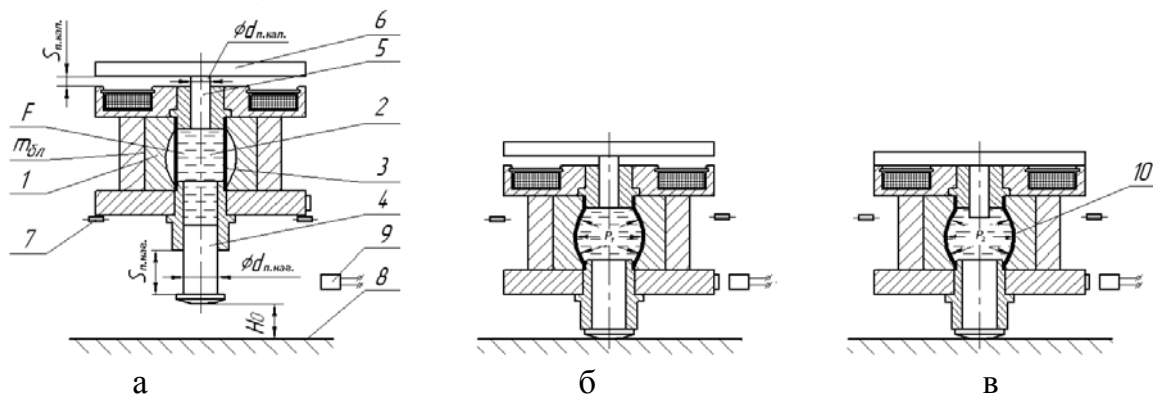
Кинематическая схема гидродинамической штамповки с калибровкой при помощи электромагнитных сил: 1 – штамповый блок; 2 – передающая среда; 3 – заготовка; 4 – нагружающий поршень; 5 – калибрующий поршень; 6 – якорь электромагнита; 7 – фиксаторы; 8 – жесткая опора; 9 – датчик положения; 10 – отштампованная деталь; $d_{п.наг.}$ – диаметр нагружающего поршня; $d_{п.кал.}$ – диаметр калибрующего поршня; $S_{п.наг.}$ – ход нагружающего поршня; $S_{п.кал.}$ – ход калибрующего поршня; H_0 – расчетная исходная высота системы; $m_{бл}$ – масса штампового блока; F – формующая камера; p_1 – давление на стадии штамповки; p_2 – давление на стадии калибровки
